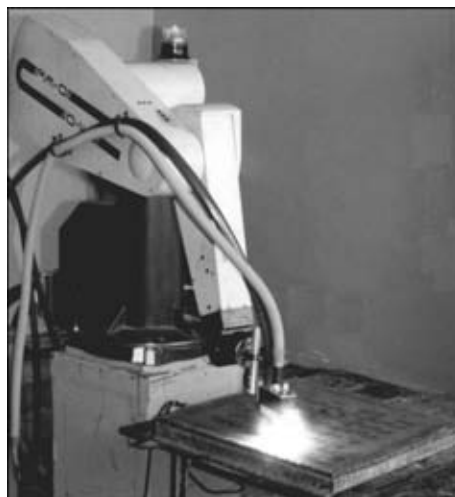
Автоматизированный комплекс для термической правки тонколистовых сварных конструкций
